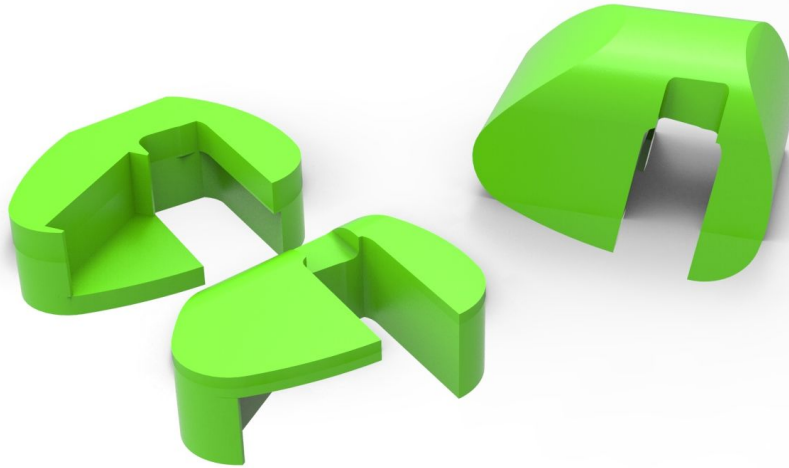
Modelo 3D de soporte de espejo. detalle de construcción.
